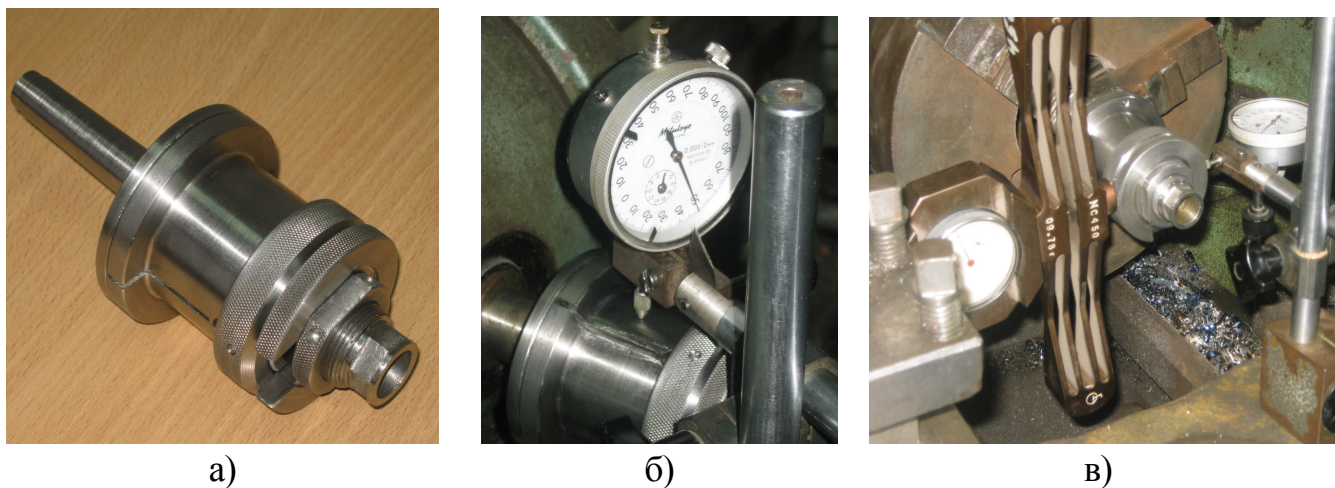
Безззорна оправка з кульковими передавально-підсилюючими елементами для проточування циліндричних заготовок (а,б), (пат. № 53027, Україна) та установка для дослідження радіального биття (в)
